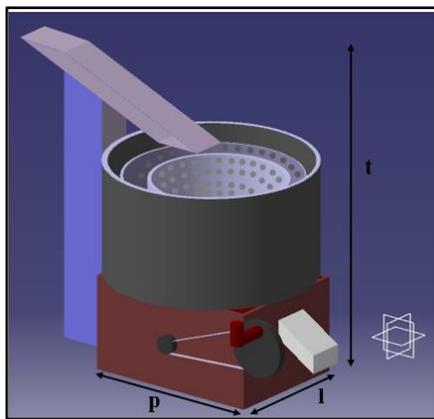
Tampak Depan Alat Penyaring Bubuk Kedelai
